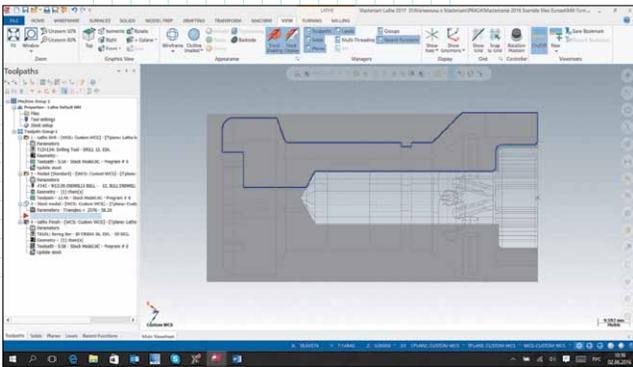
Обновленная (с учетом фрезерной операции) токарная заготовка
